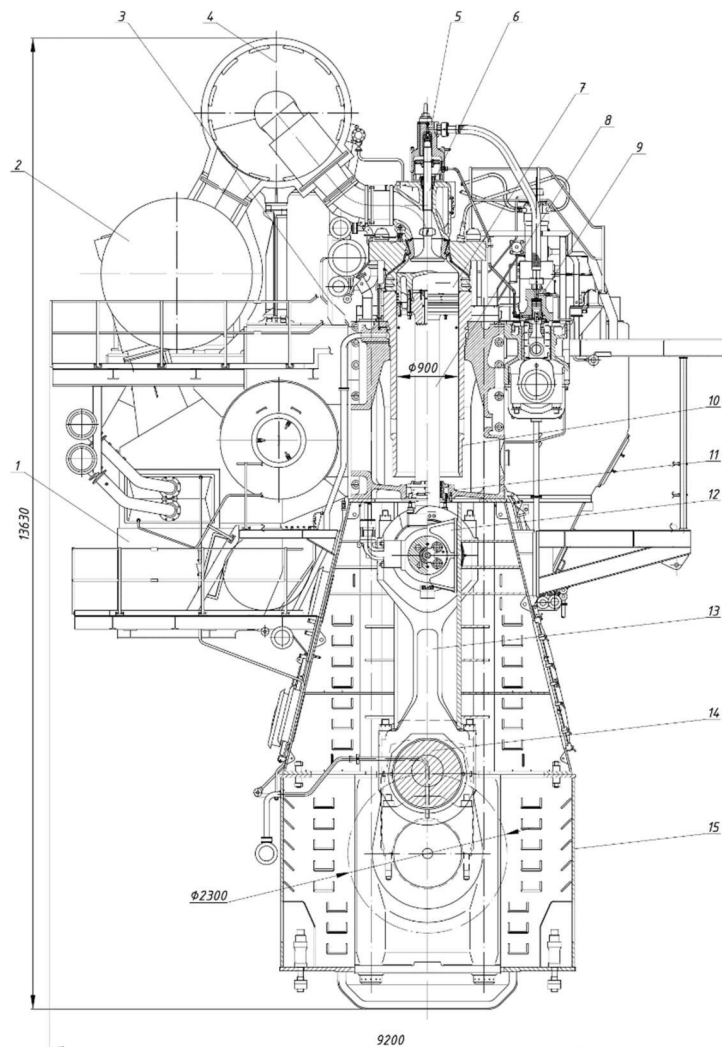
Поперечний розріз двигуна 6ДКРН90/230: 1 – ОП; 2 – турбокомпресор; 3 – ПНВТ; 4 – впускний ресивер; 5 – охолоджувач приводу випускного клапана; 6 – випускний клапан; 7 – поршень; 8 – шток поршня; 9 – модулятор приводу клапана; 10 – втулка циліндра; 11 – сорочка циліндра; 12 – крейцкопф; 13 – шатун; 14 – колінчастий вал; 15 – фундаментна рама
